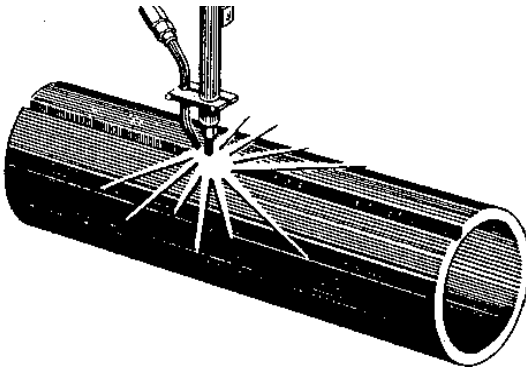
(C) Um dos muitos tipos de soldagens automáticas.
